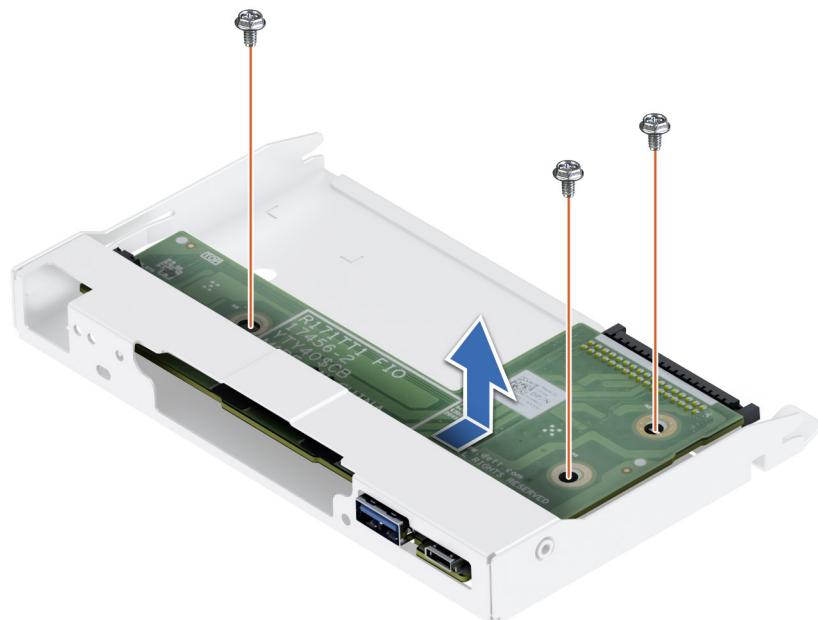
Entfernen der Bedienfeldbaugruppe
